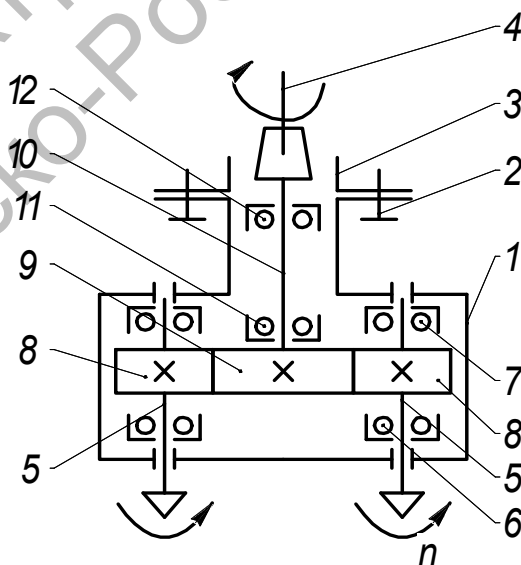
Традиционная головка многшпindelная (настоящее): 1 – корпус; 2 – болты; 3 – пиньоль; 4 – ось шпindelа станка; 5 – рабочие инструментальные шпindelы; 6 и 7 – передние и задние опоры рабочих шпindelов; 8, 9 – зубчатые колеса; 10 – приводной вал с опорами; 11, 12 – опоры
